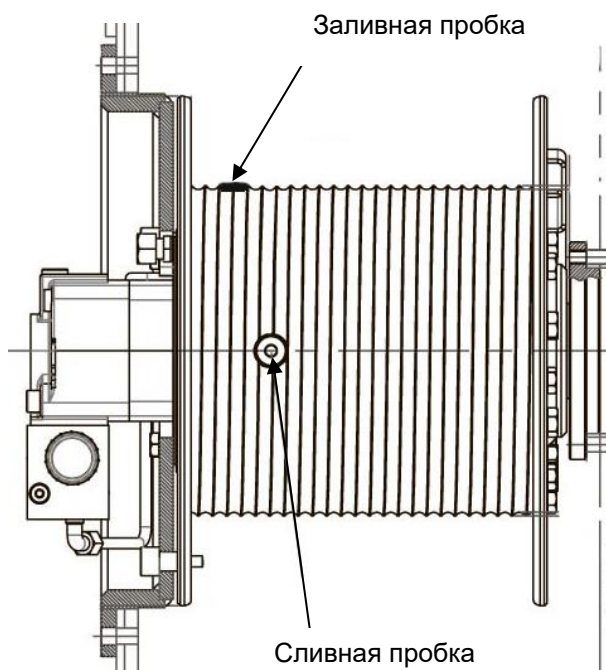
Лебедка с расположением сливной и заливной пробок на рабочей цилиндрической поверхности барабана
